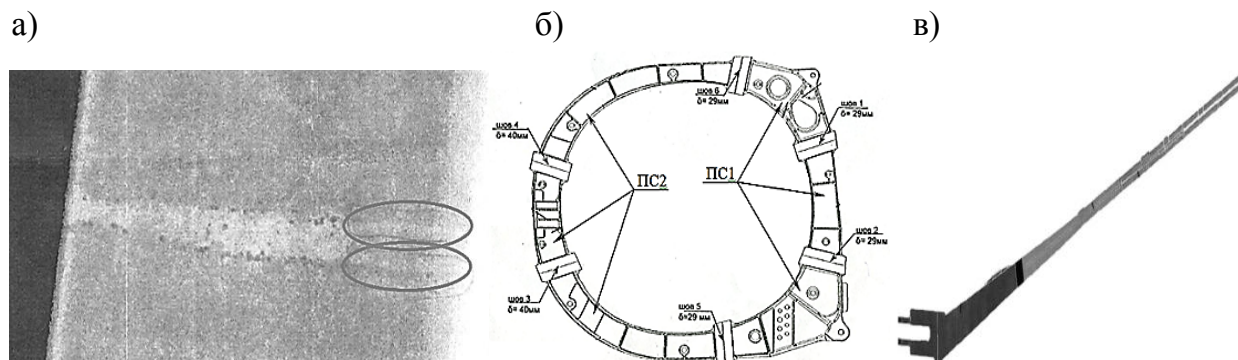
Внешний вид «темных полос» на рентгенограмме сварного соединения (а) и силовых элементов конструкций из титановых сплавов: шпангоута (б), лонжерона (в)
